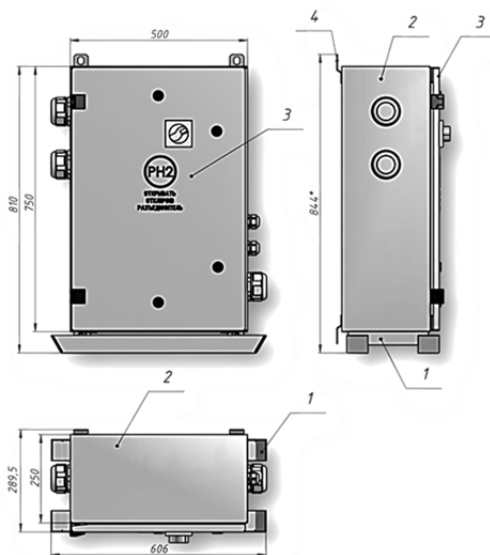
Общий вид ПРН с габаритными размерами
